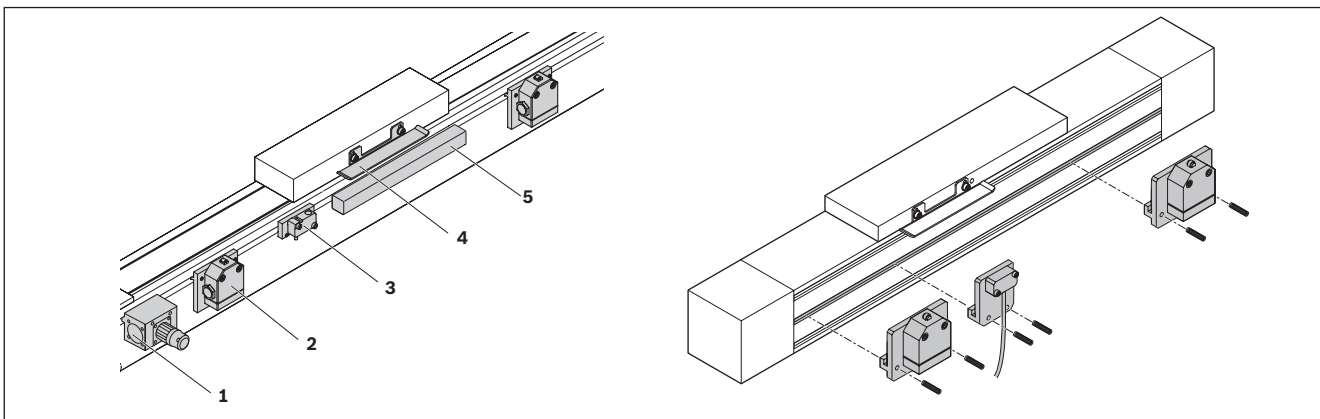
Vue d'ensemble interrupteur mécanique, capteurs inductifs, prise-fiche, goulotte de câble, équerre de contact
